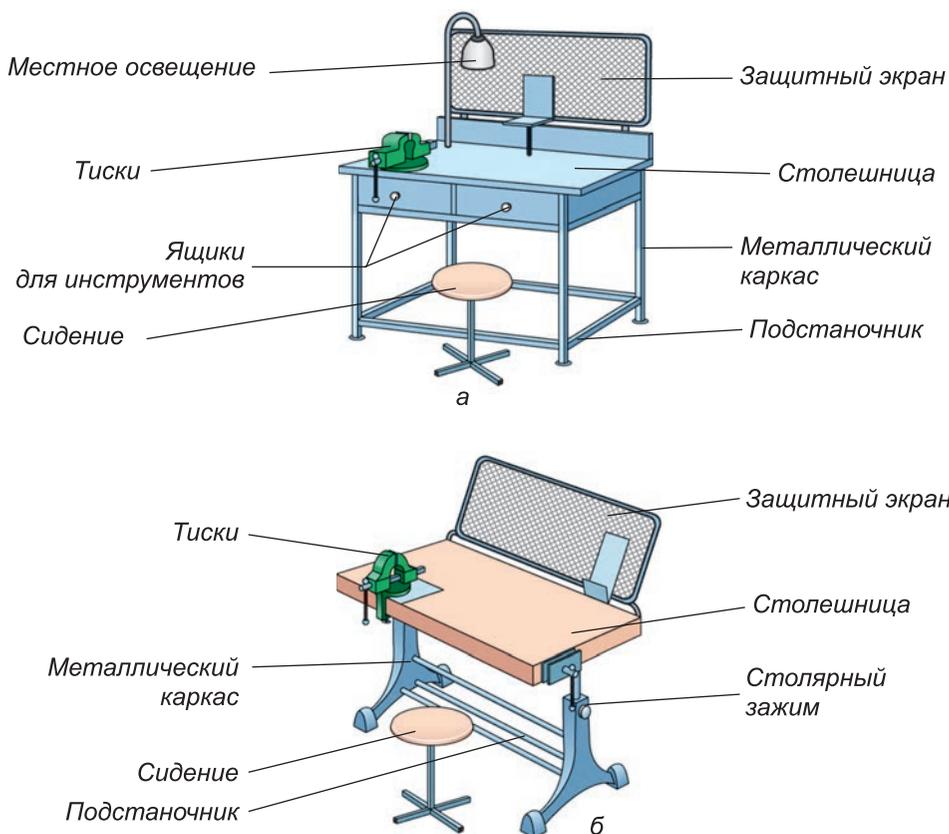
Станки: а – слесарный одноместный; б – комбинированный одноместный
